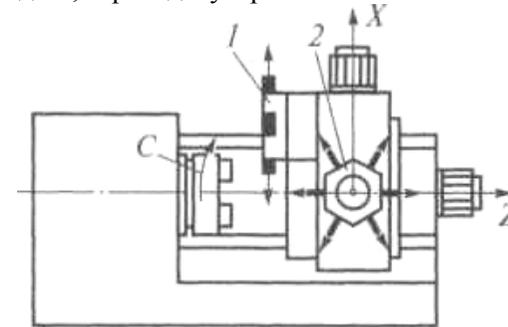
Токарный станок с ЧПУ, где 1, 2 – револьверные головки
